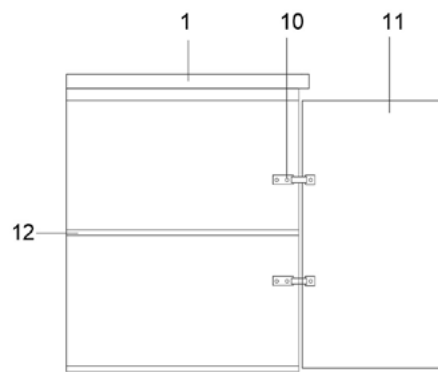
Detalle constructivo mueble de cocina con madera de pino
